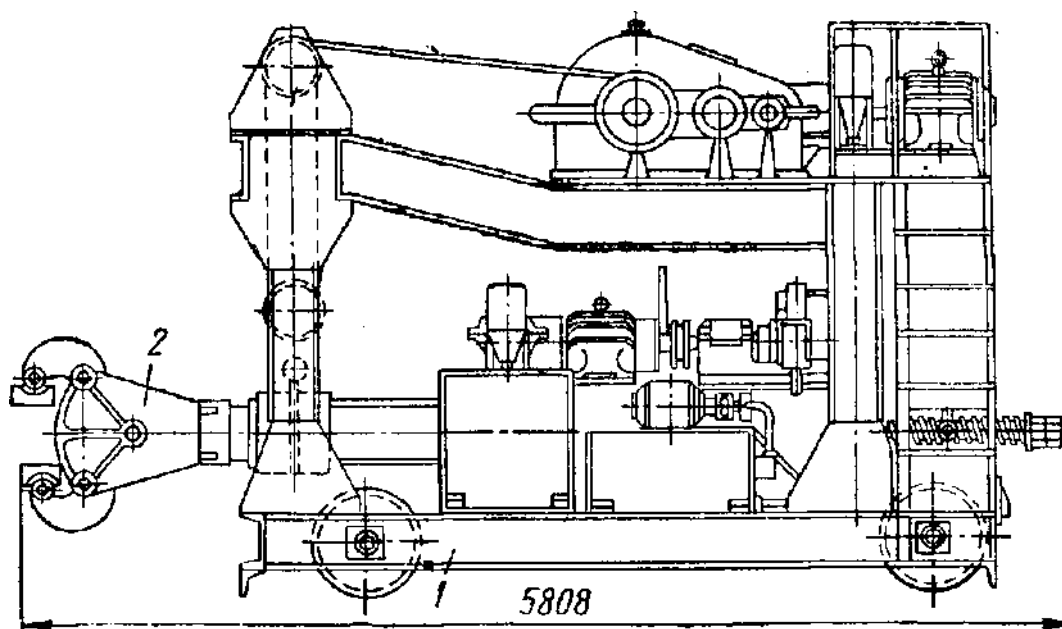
Загальний вид підложного рейкового маніпулятора
